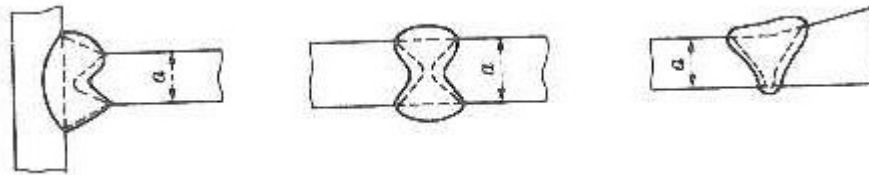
完全溶込み開先溶接の理論のど厚
